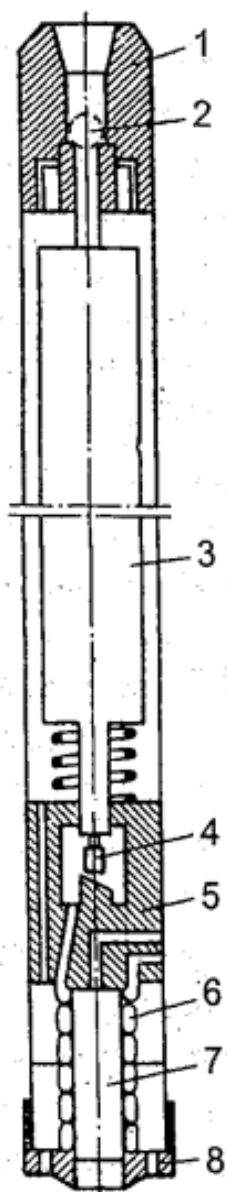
Схема буровой установки для получения керногазовых проб с замораживанием керногазовой пробы
